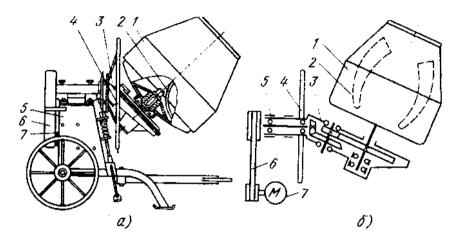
Бетоносмеситель с опрокидным барабаном: а – конструктивная схема; б – кинематическая схема
